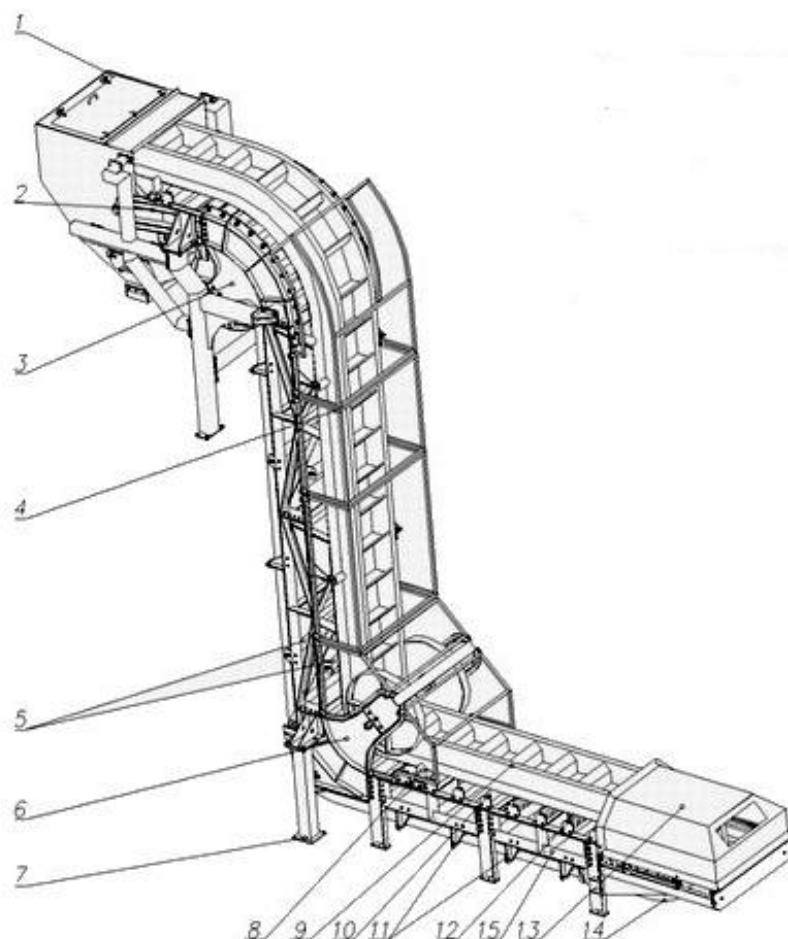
Конструктивная схема Z-образного конвейера:
